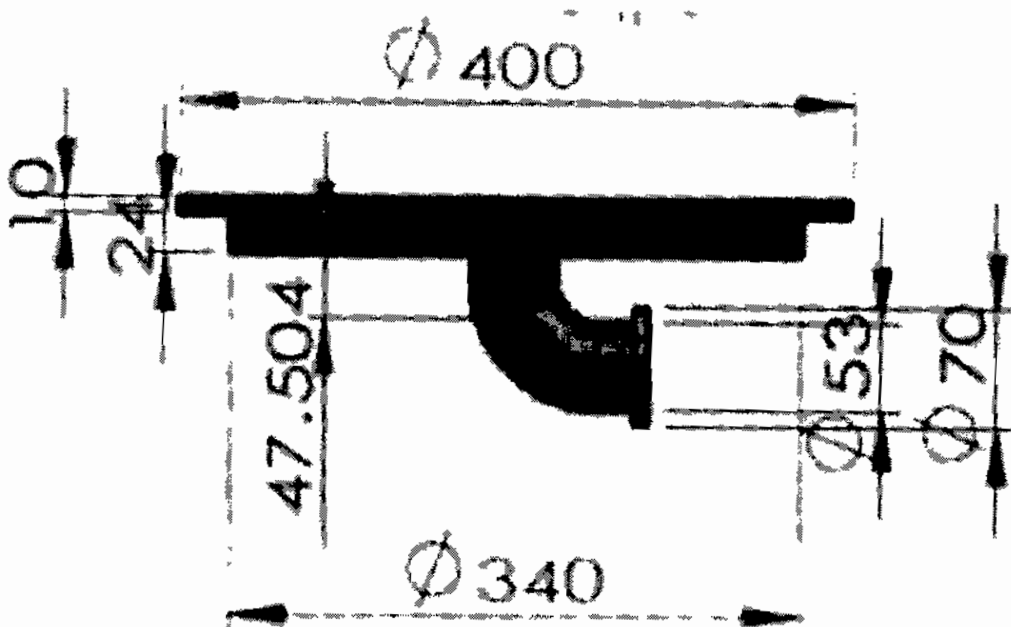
ภาพ drawing ฐานรองชิ้นงาน (แบบสั้น)
